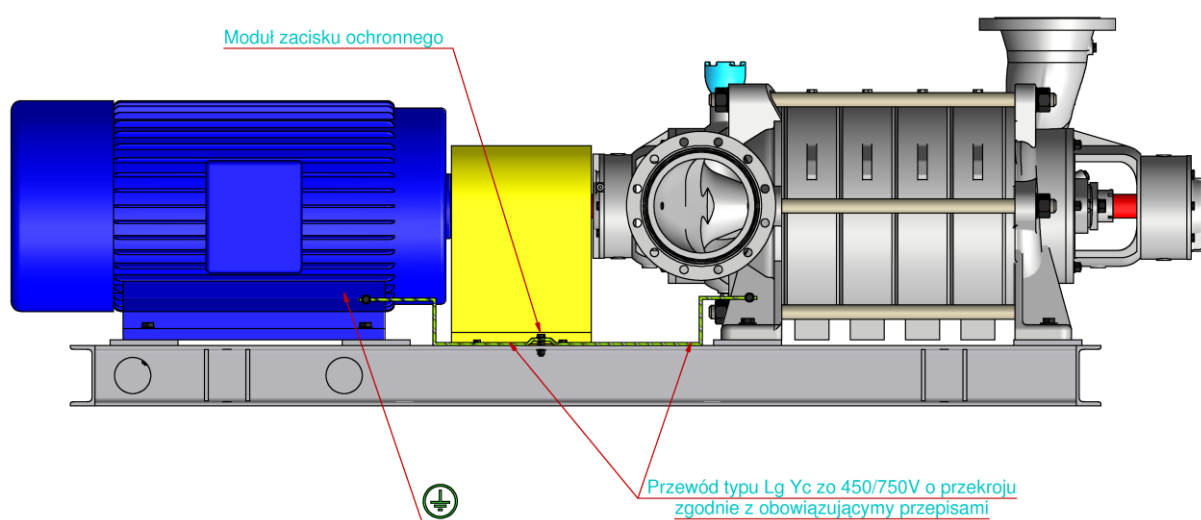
zobrazuje vzorové zapojení zemnicích kabelů. Skutečná zapojení se od vzorového mohou lišit.
